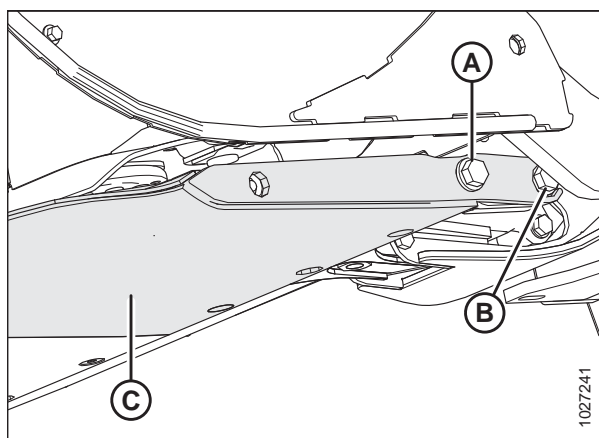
Левый наружный защитный палец – Вид сбоку
